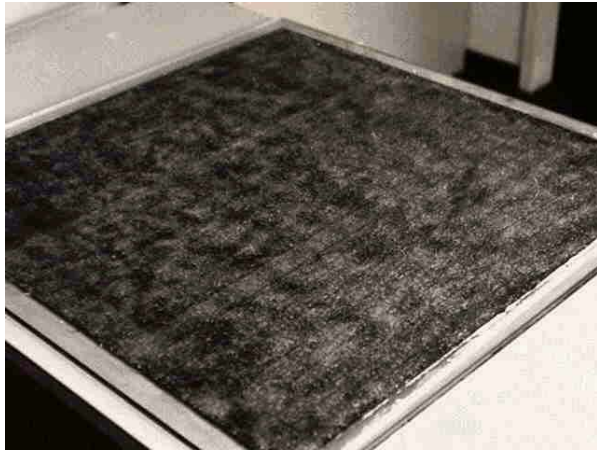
Deckschicht mit Isolierung und Abreißgewebe
